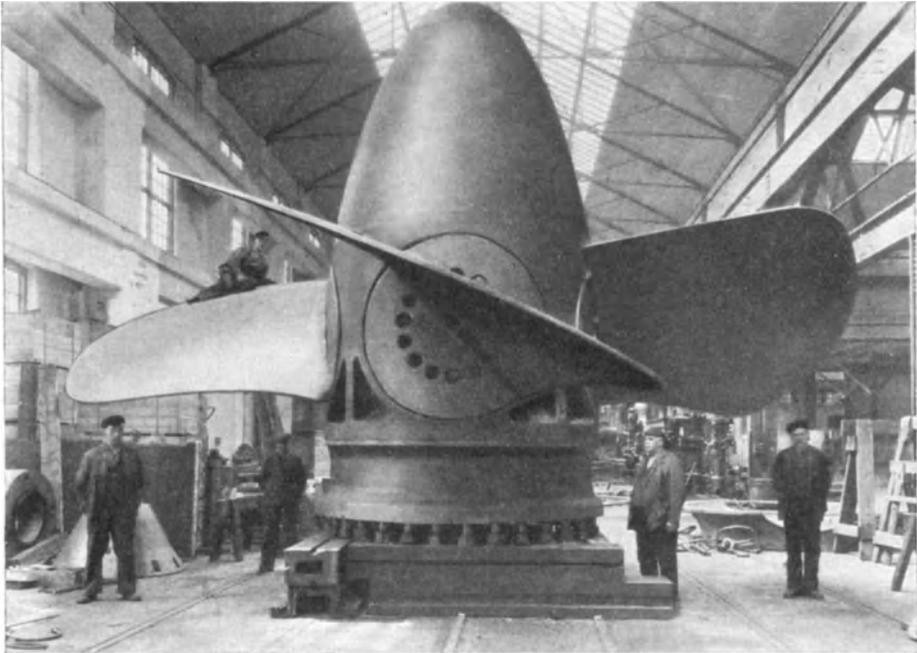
Laufrad der Kaplan-turbine in Vargön, Schweden. — Durchmesser 8 Meter.
